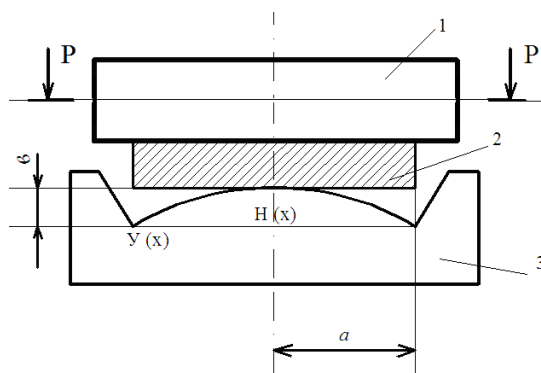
Схема процесса выдавливания заготовки в матрицу
